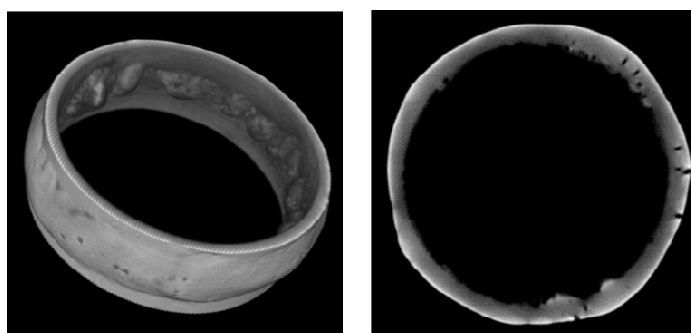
Трехмерная визуализация сварного соединения (слева), сечение исследуемого сварного шва (справа)
